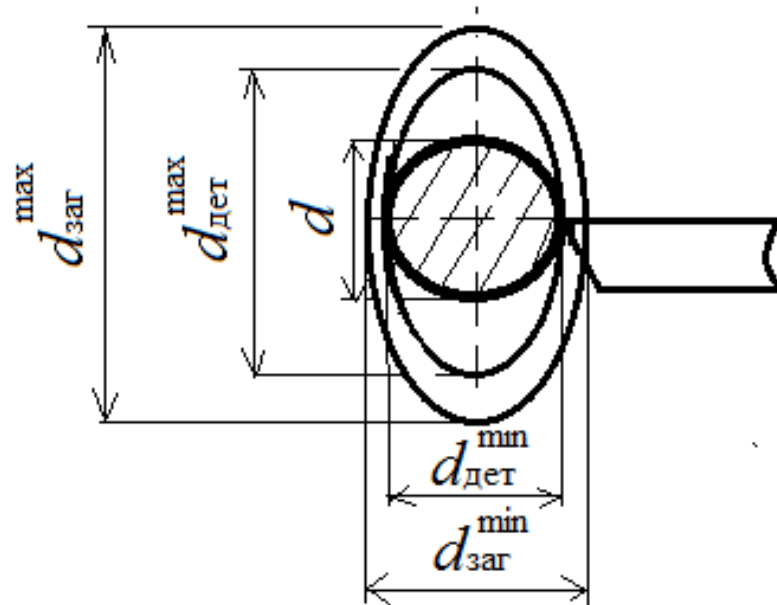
Зміна форми обробленої деталі у порівнянні із похибками форми заготовки
